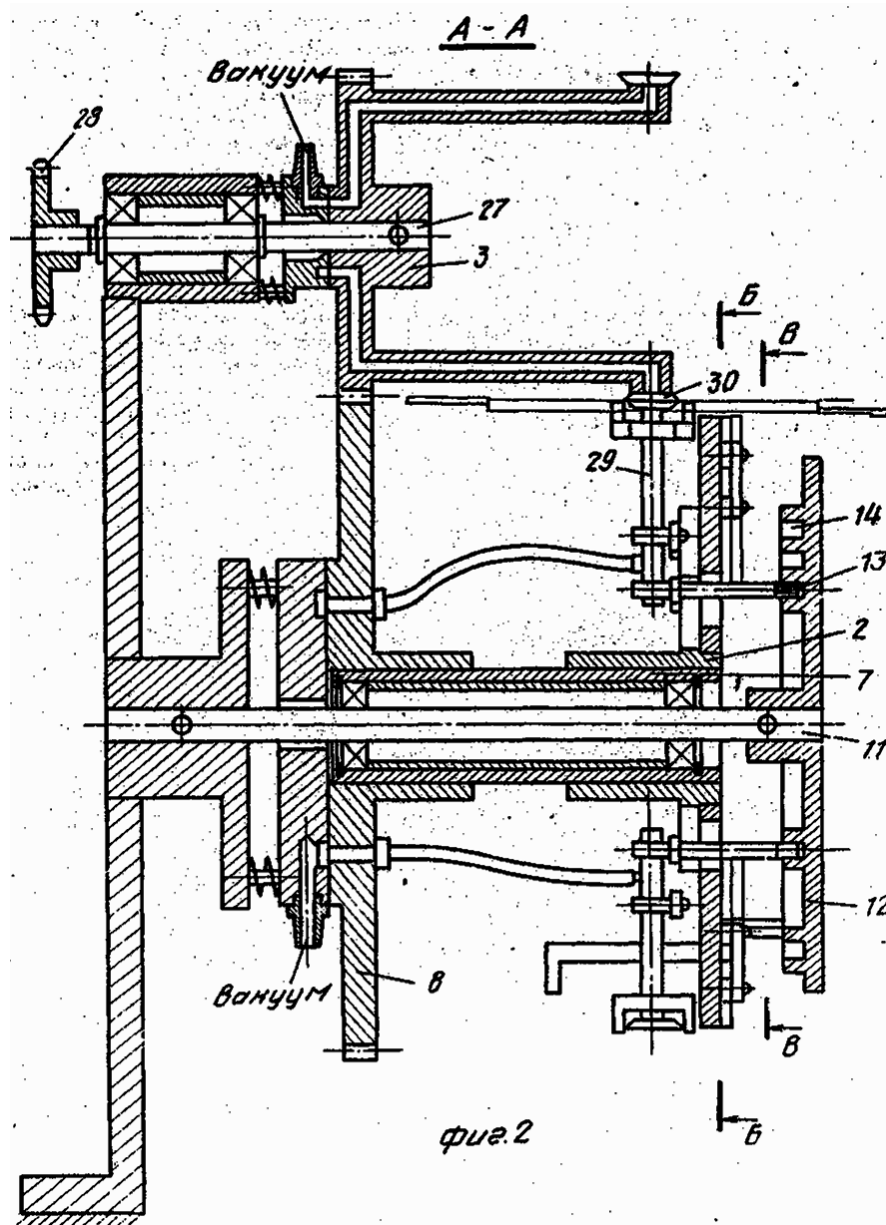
Пристрій для поштучної подачі й формування картонних пачок із плоско складених заготовок
